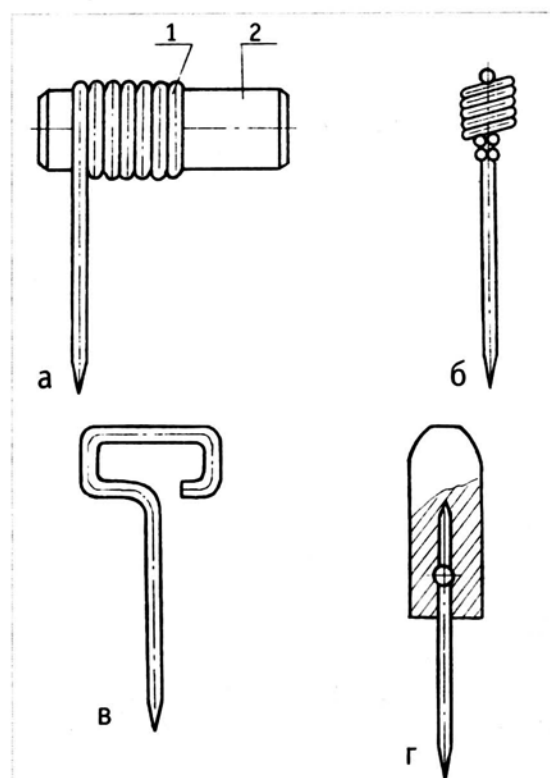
Шилья самодельные: а — из пружины: 1 — пружина; 2 — деревянная рукоятка; б — проволочное с накрученной проволочной рукояткой; в — проволочное, типа ключа для открывания консервов; г — из проволоки, гвоздя или спицы
